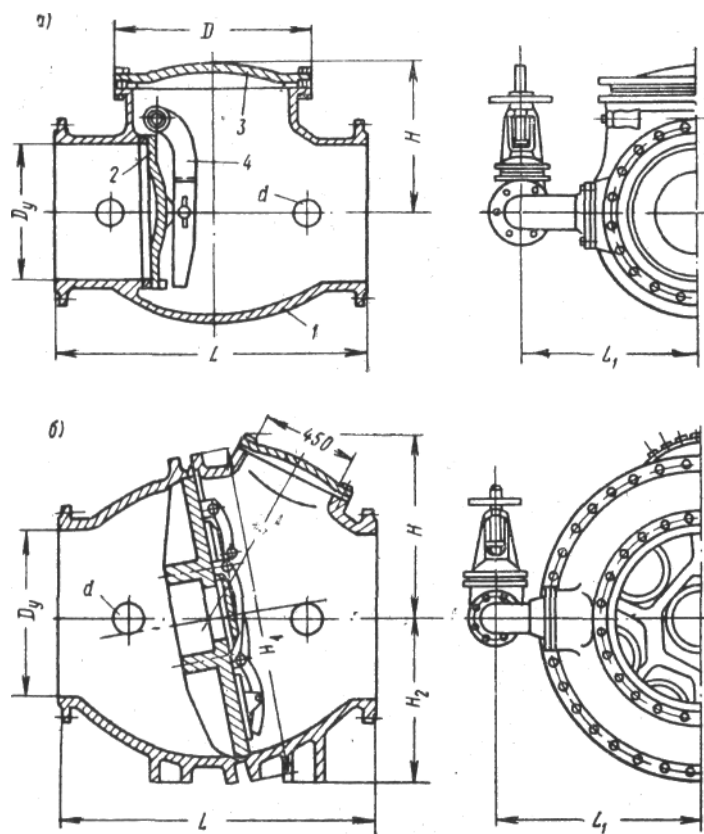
Клапан зворотний поворотний 19с38нж:
